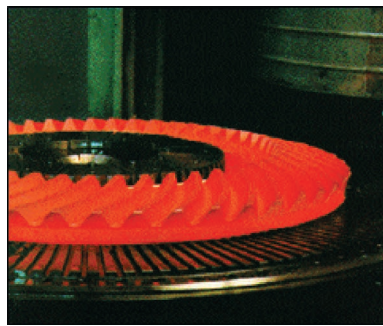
Закалка ведомого конического колеса в закалочном устройстве.
